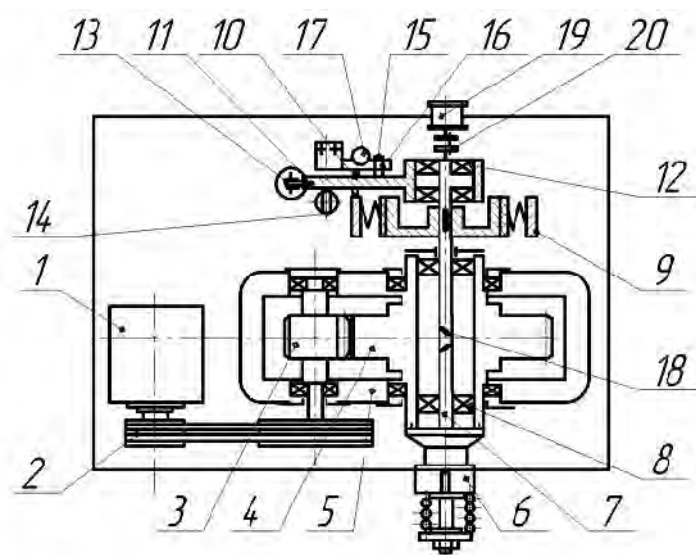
Схема лабораторной установки для испытания муфт
